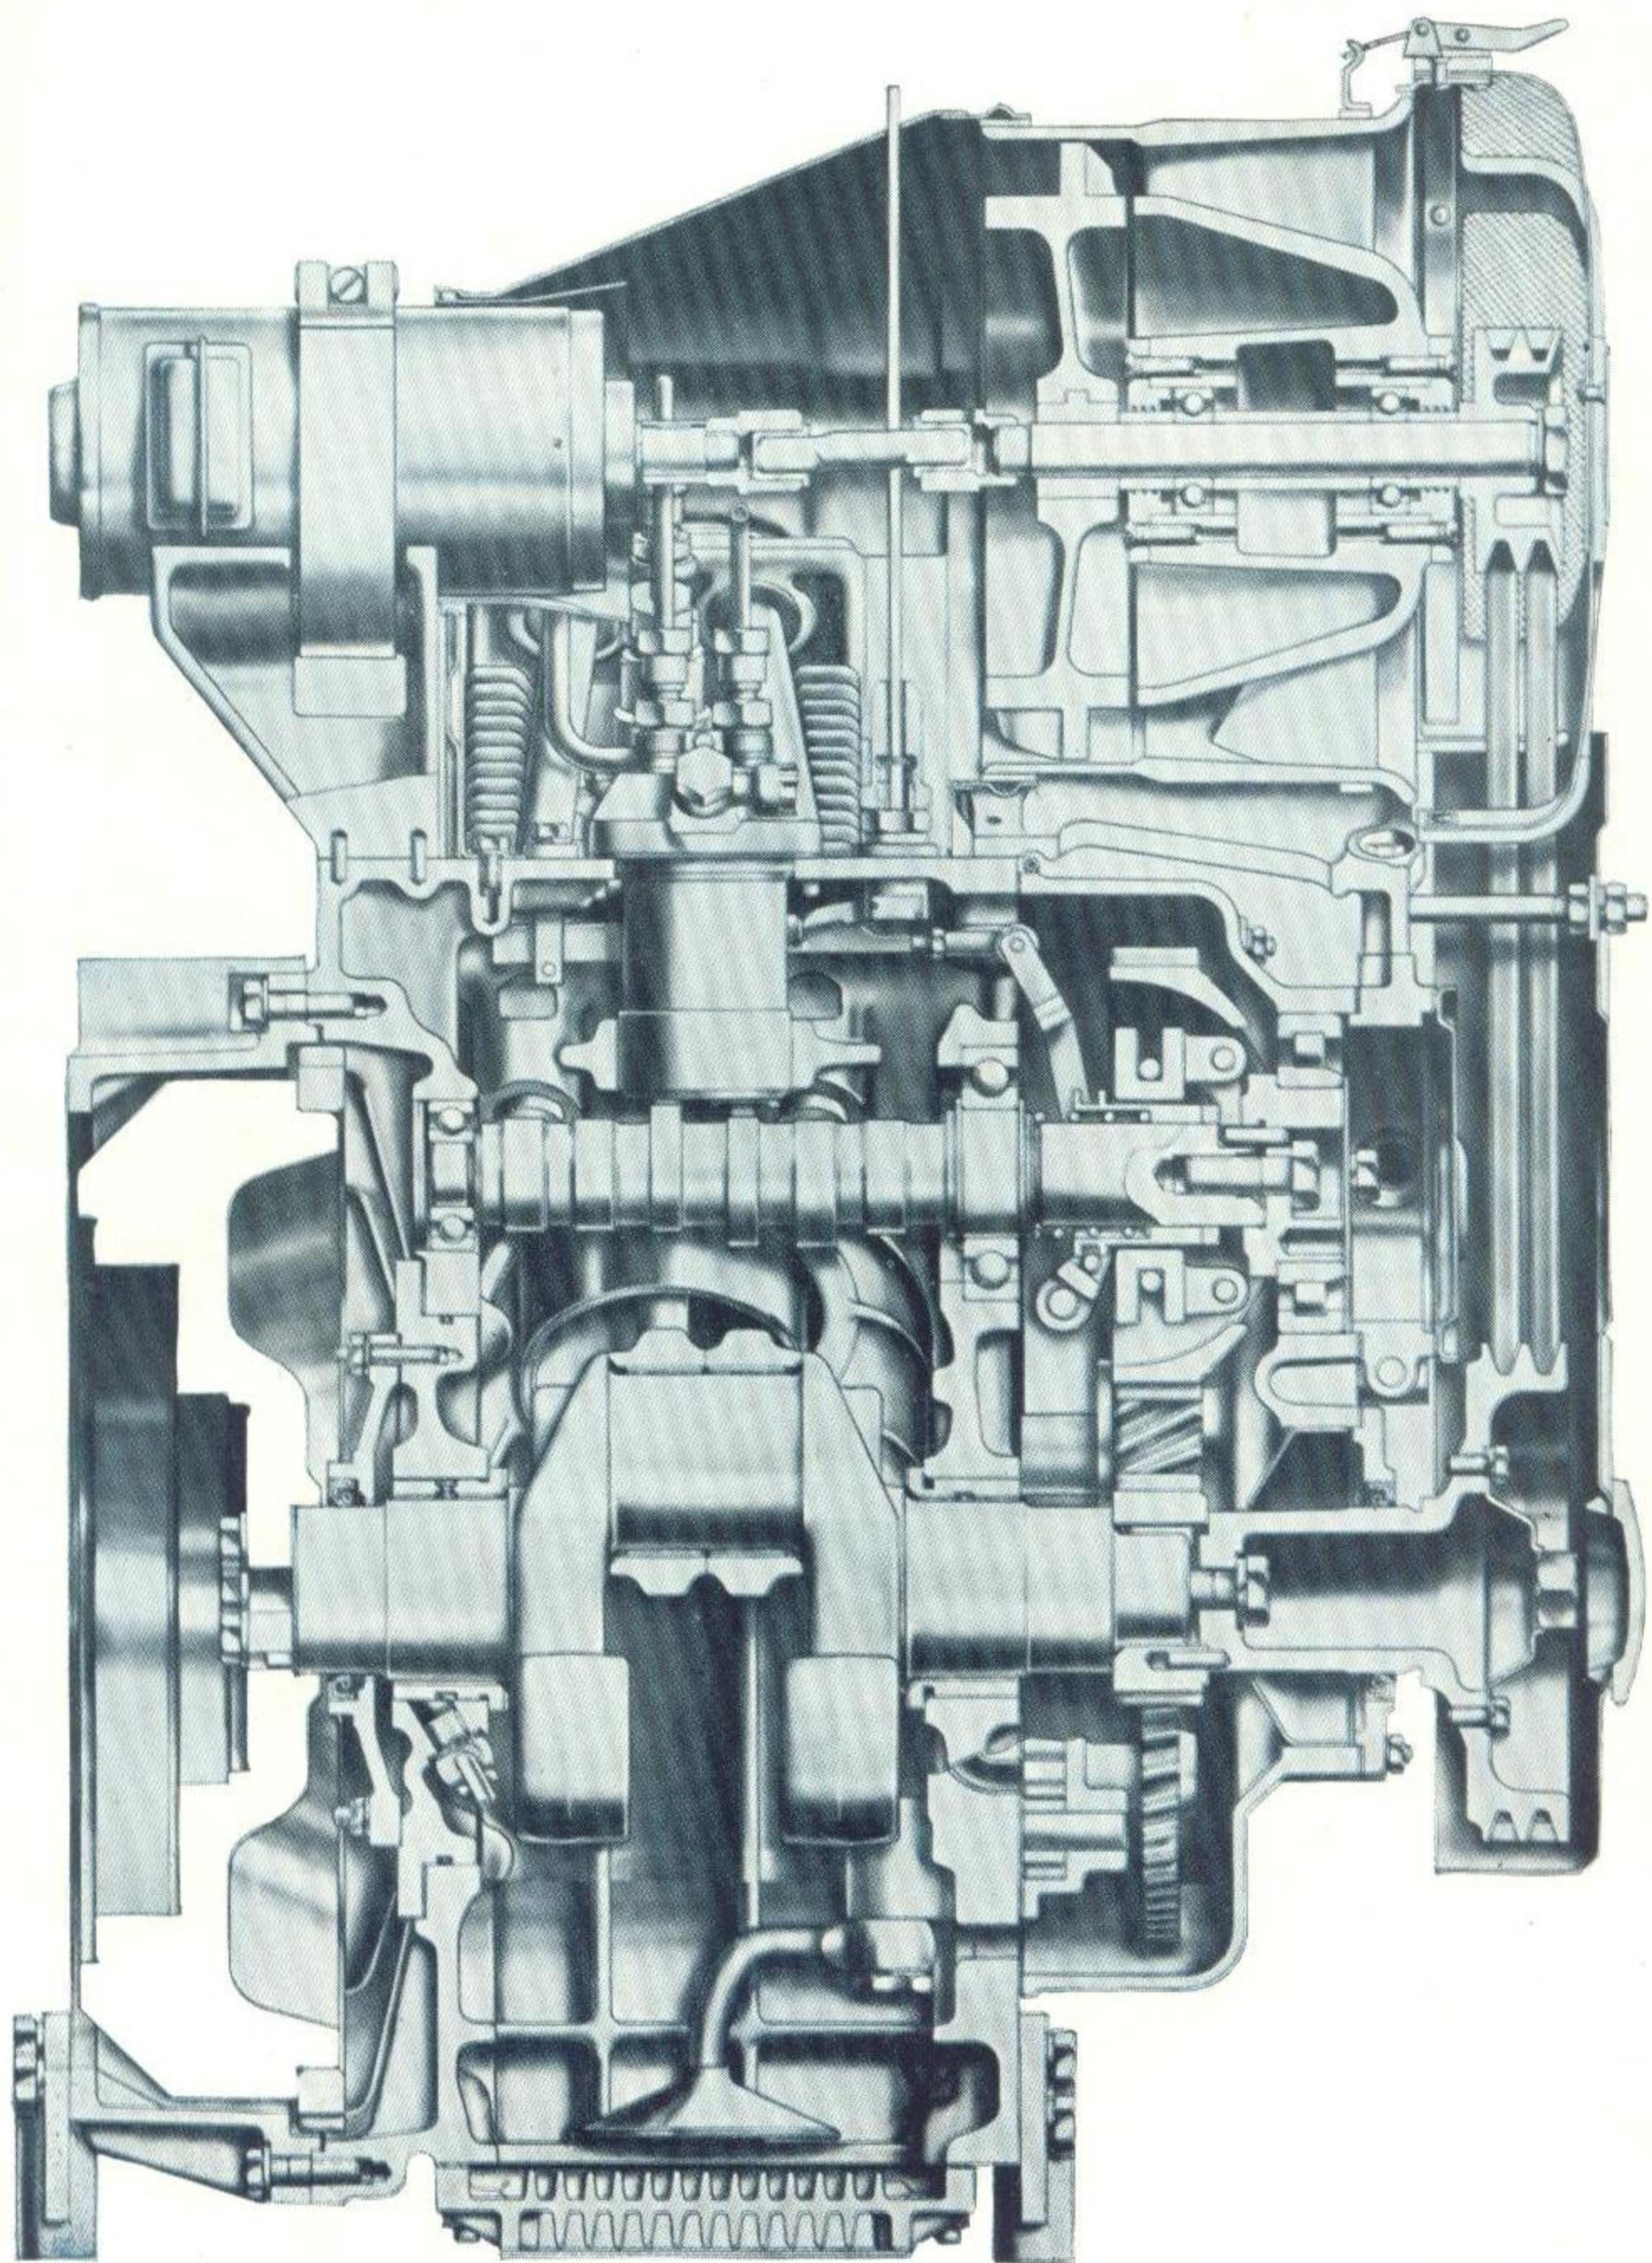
Motor 1 KVD 8 SL, podélný řez
